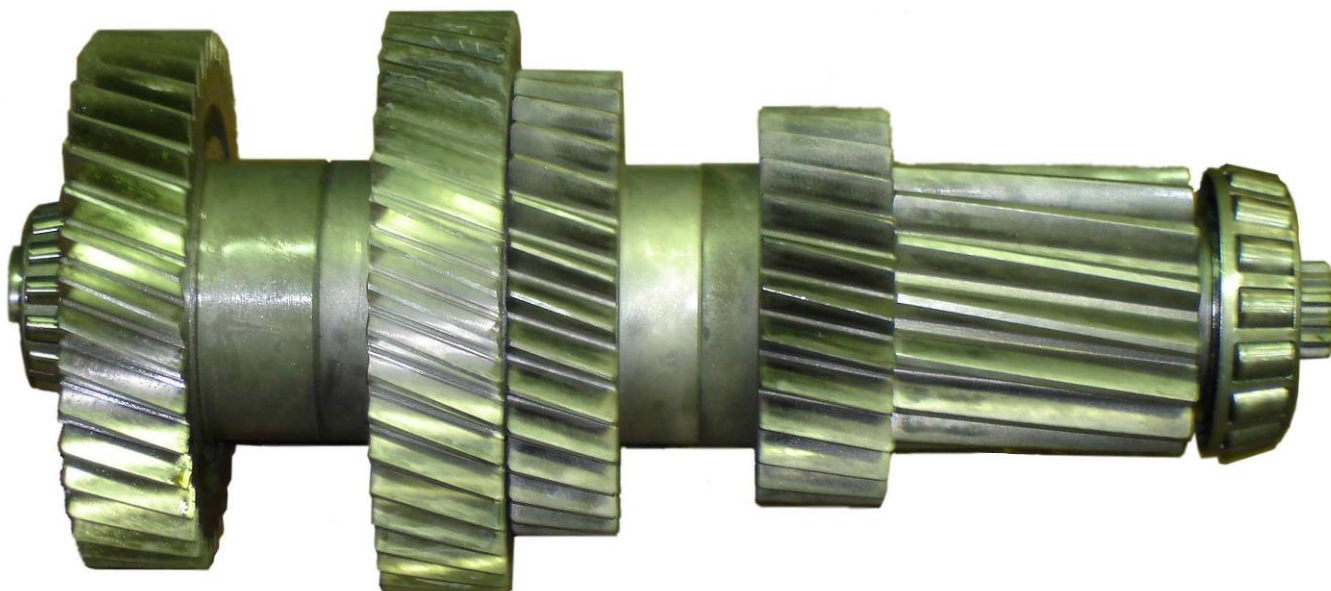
Вал промежуточный в сборе, дет. 239.1701047, КП ЯМЗ-239
